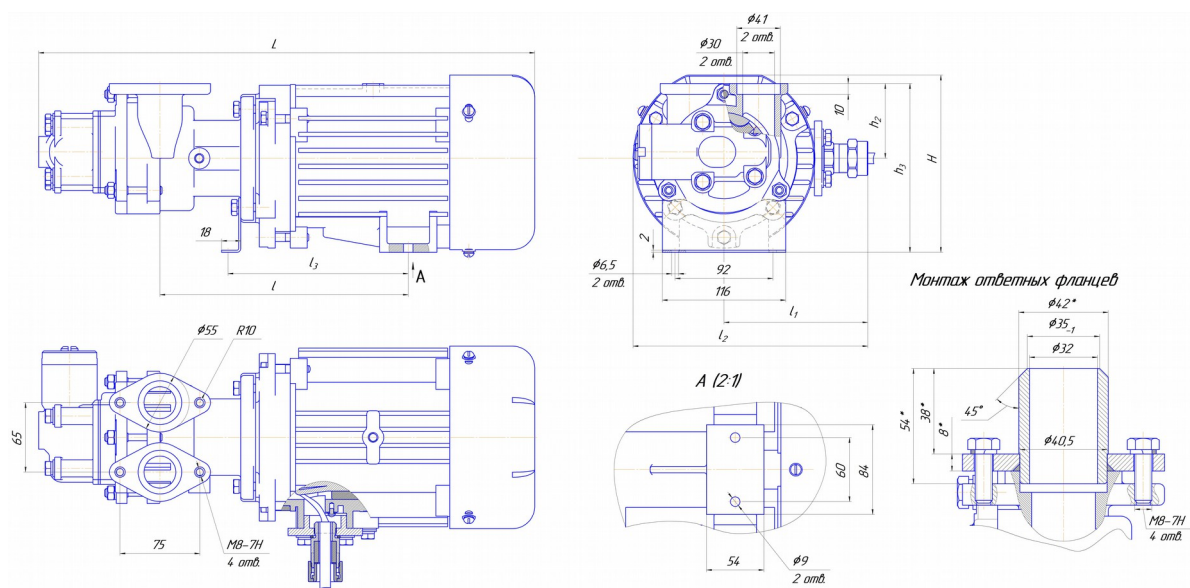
Габаритные и присоединительные размеры электронасосов БШМ-20, БШМ-40, БШМ-50, БШМ-100 (без лап), с вертикальным расположением входного/ выходного патрубков корпуса (для комплектации ТРК).
